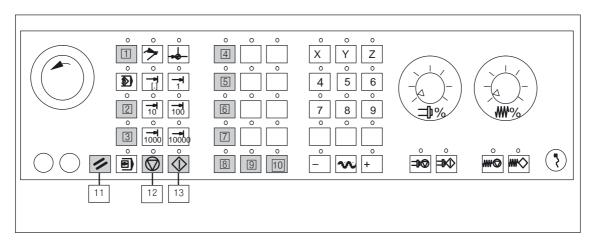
Tastenbelegung Maschinensteuertafel 19"
